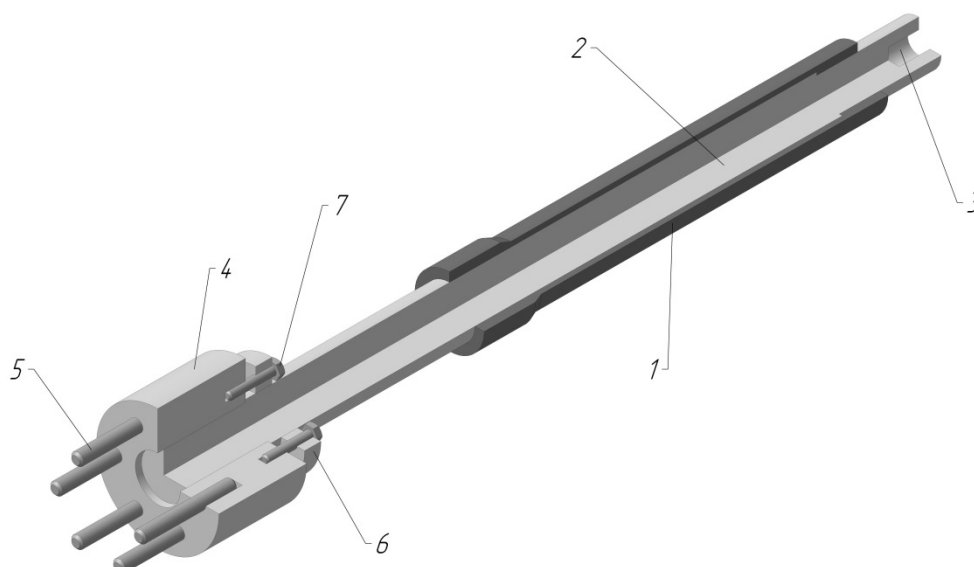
Схема установки трубы на раскатном стане:
